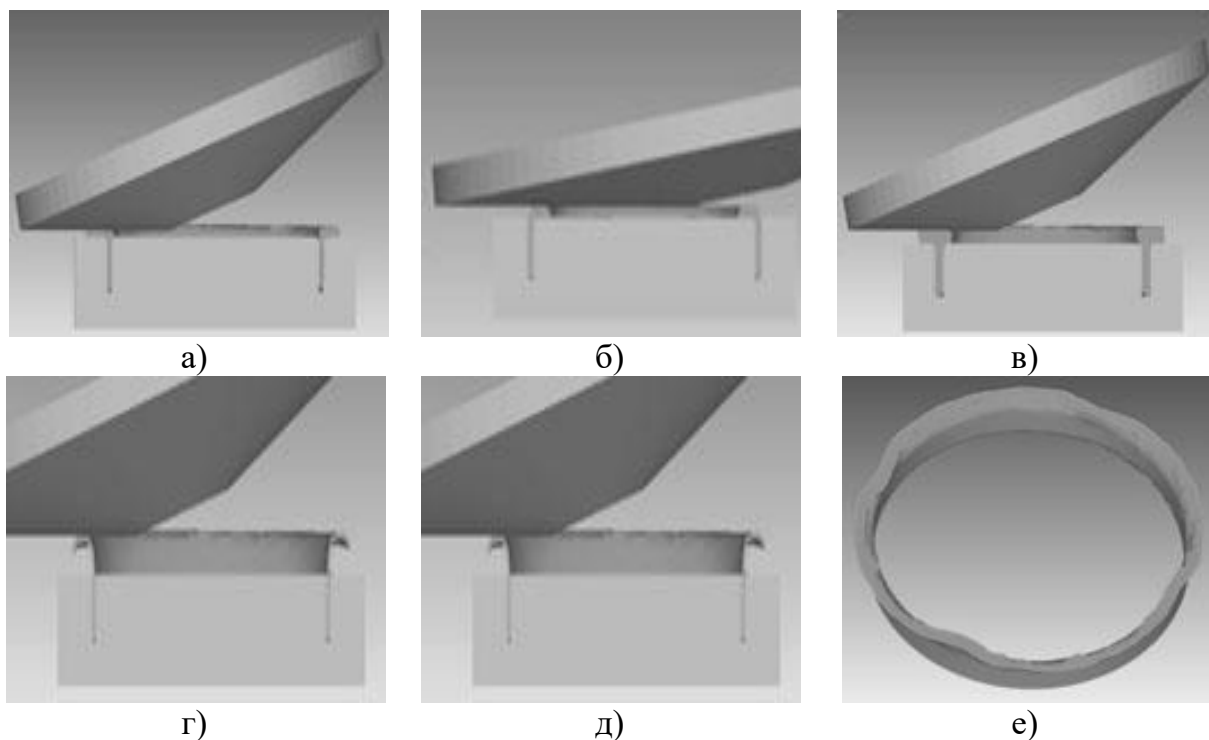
Виды формоизменения трубной заготовки при торцевой раскатке
